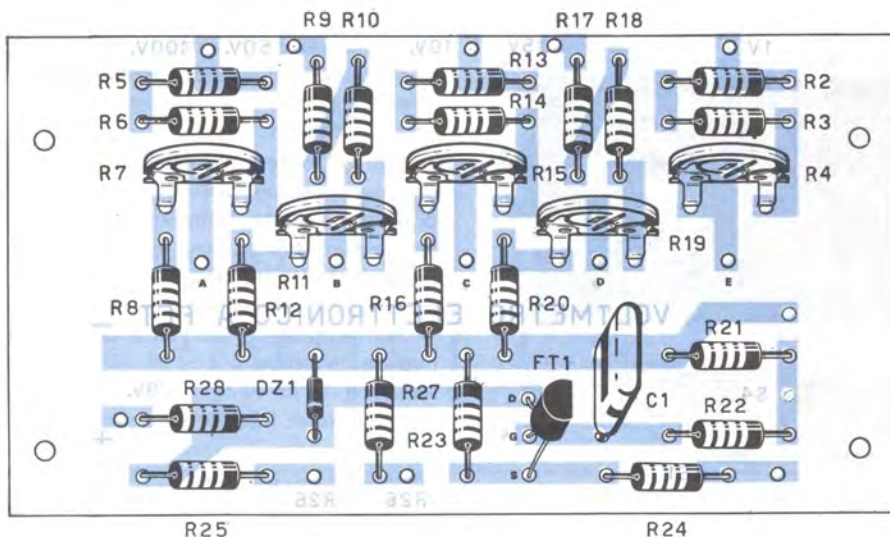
In alto, è visibile lo schema pratico di montaggio del circuito stampato vista dal lato dei componenti.
